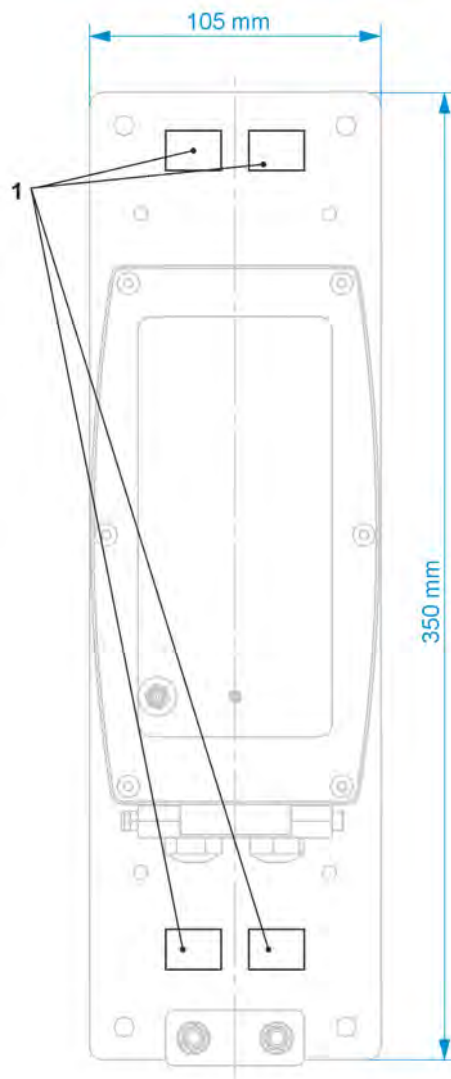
Fixation au mât à l'aide de colliers de serrage
